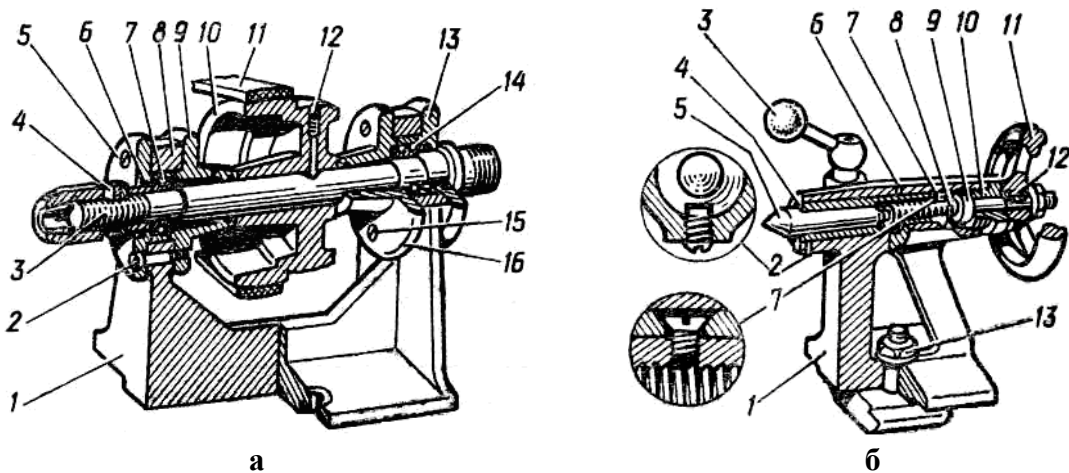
Конструктивні частини токарного верстата для обробки деревини
